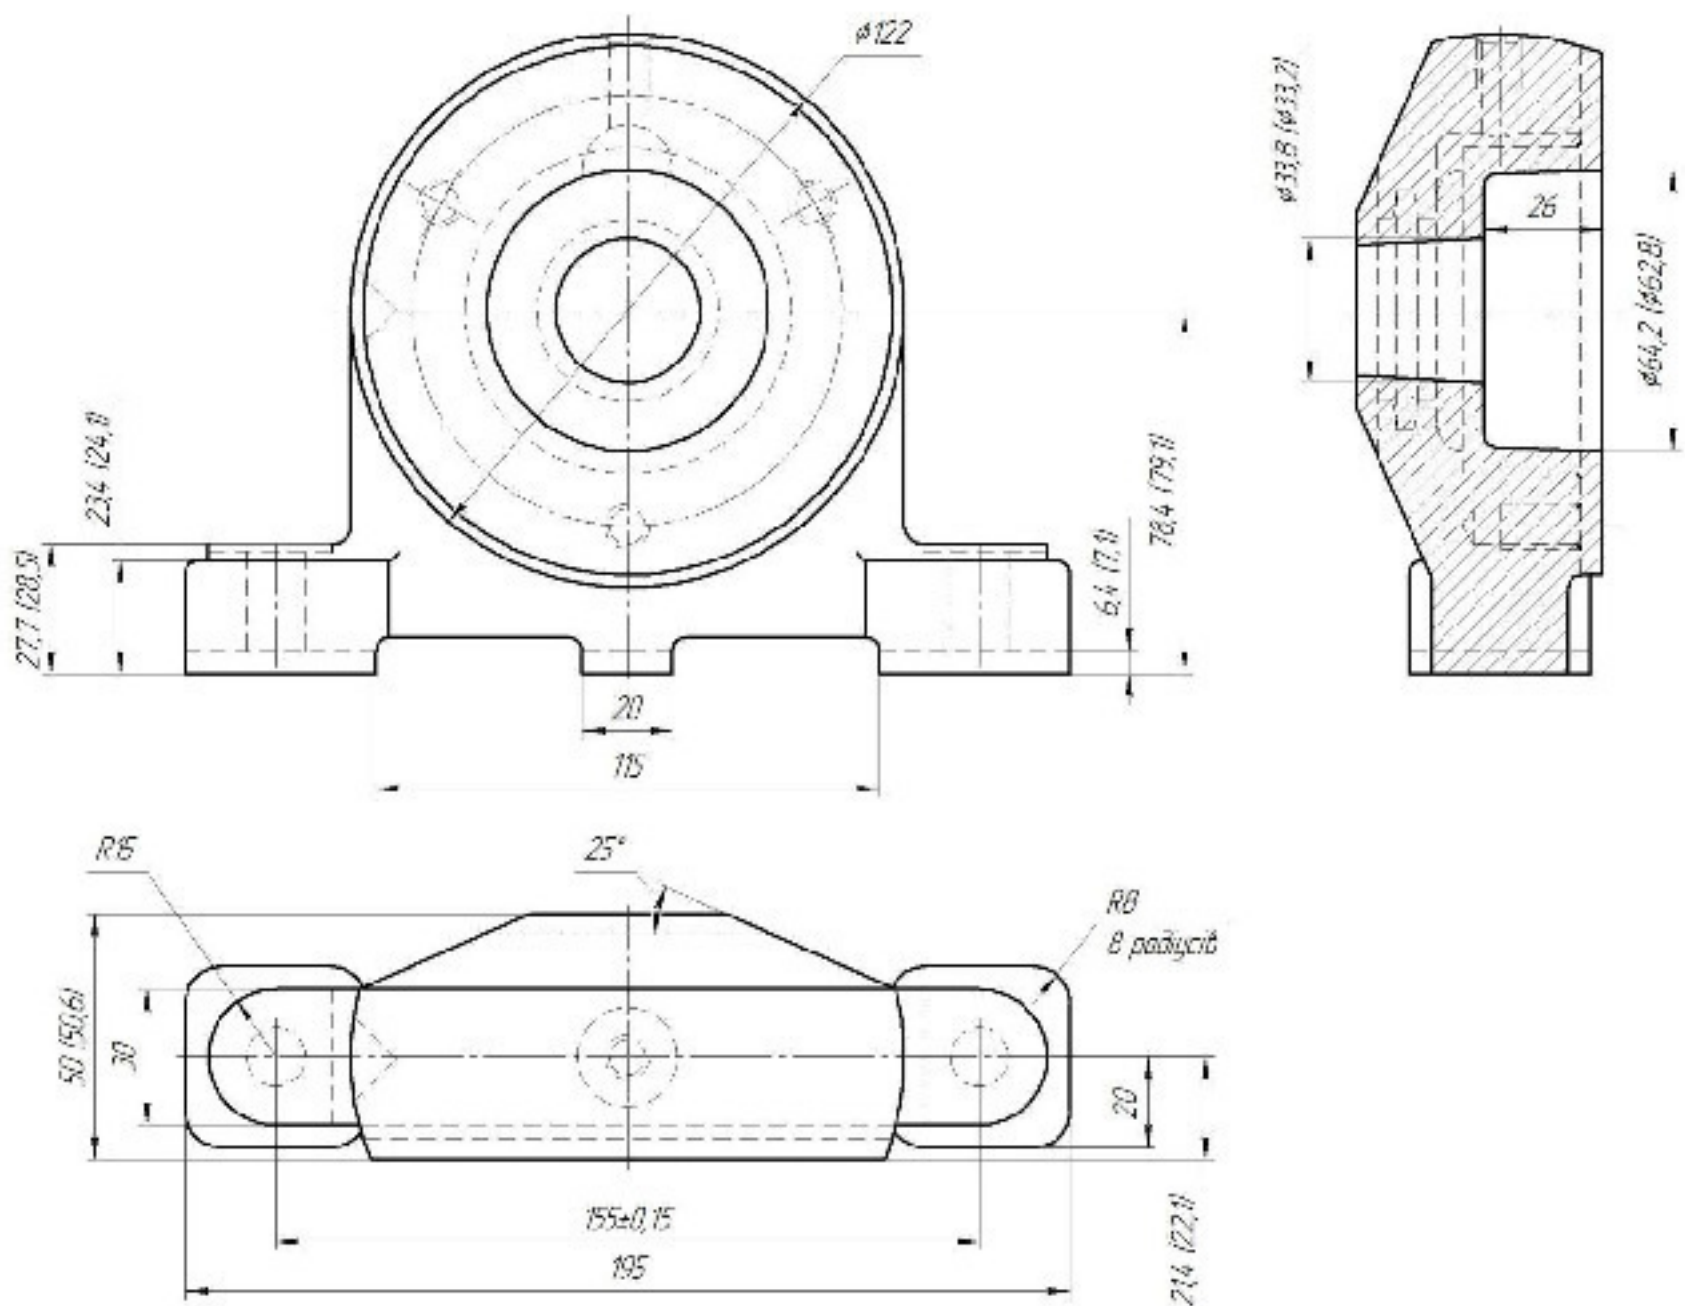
Ескіз заготовки, виготовленої литтям в піщано-глинисті форми з машинним формуванням суміші (оболонкові форми)
